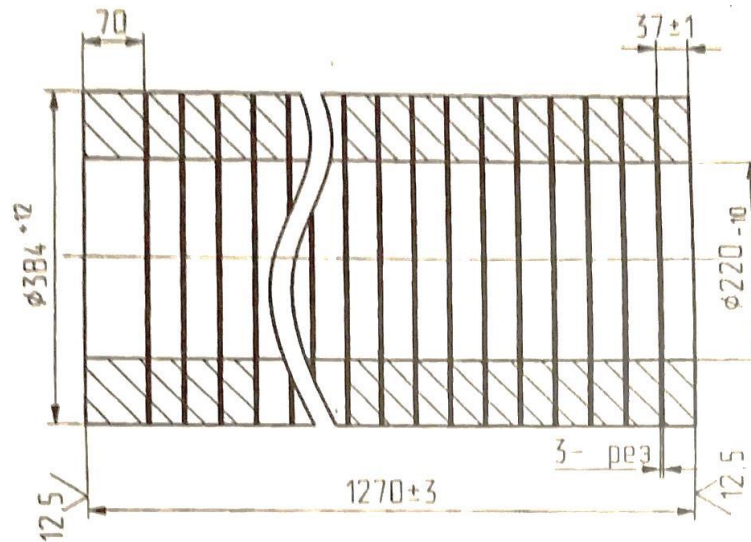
Заготовка  $D=384$  мм на дисковые ножи получаемая на установке ЭШП
